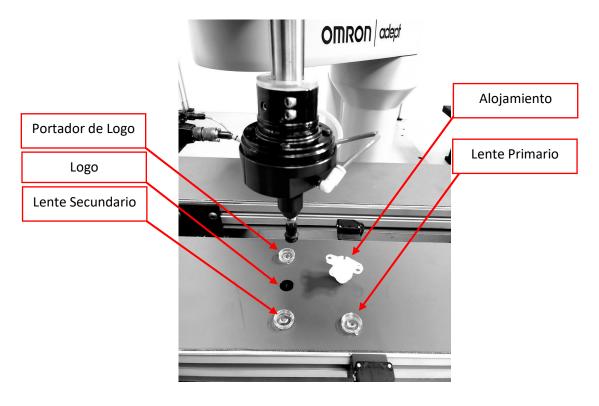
Pruebas ensamble de dispositivo Robot eCobra 650 Pro.
